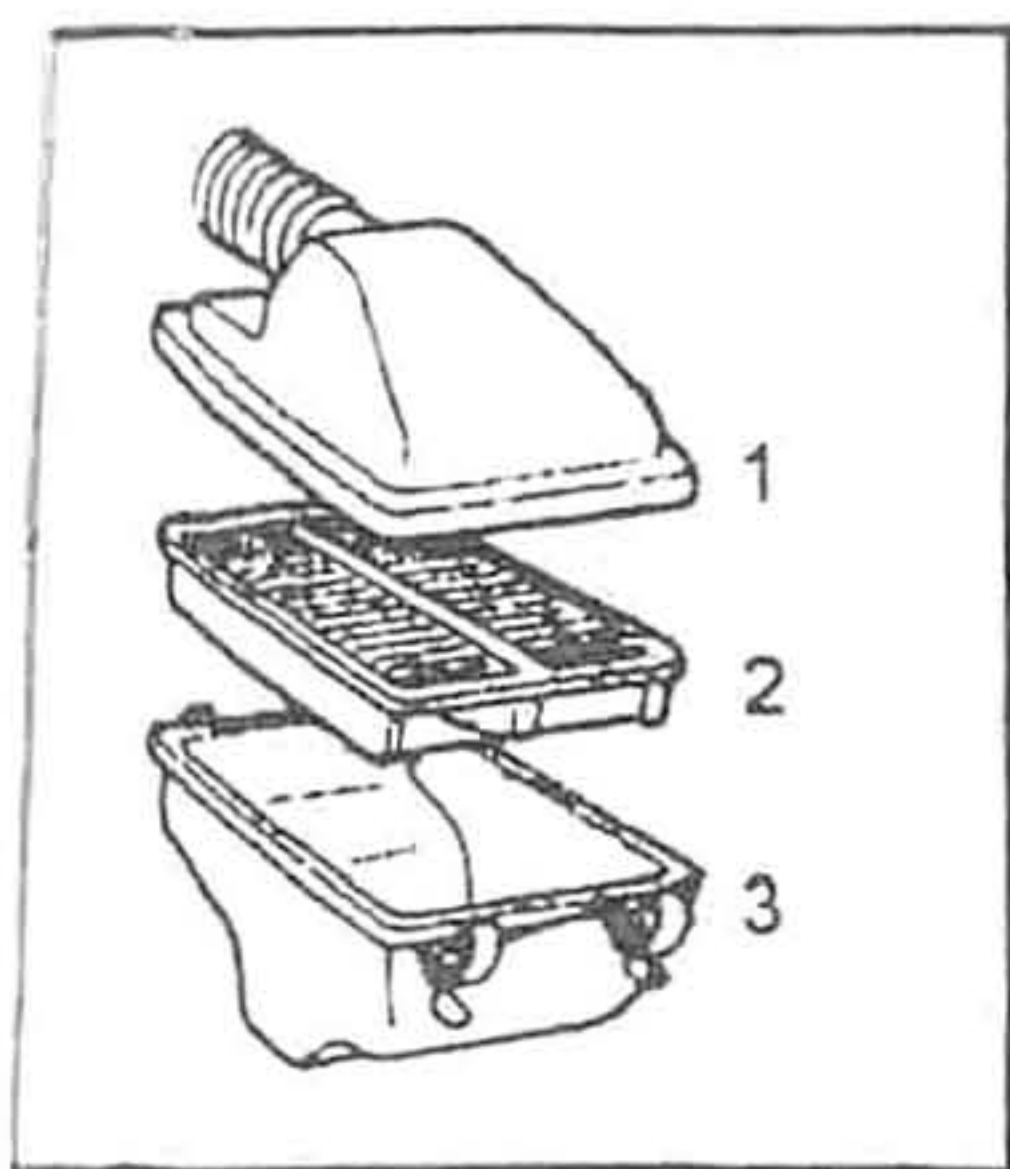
1. Крышка. 2. Фильтрующий элемент. 3. Корпус.
